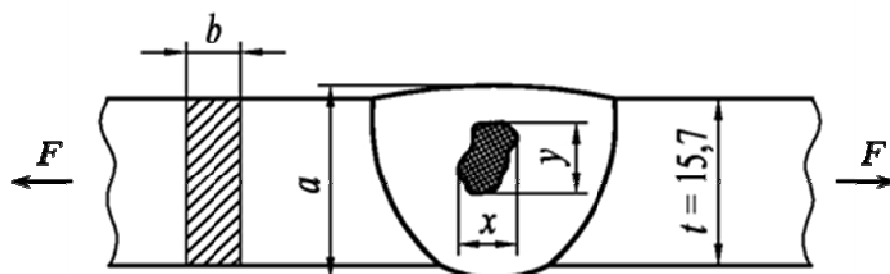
Эскиз образца стыкового сварного соединения с внутренним дефектом
